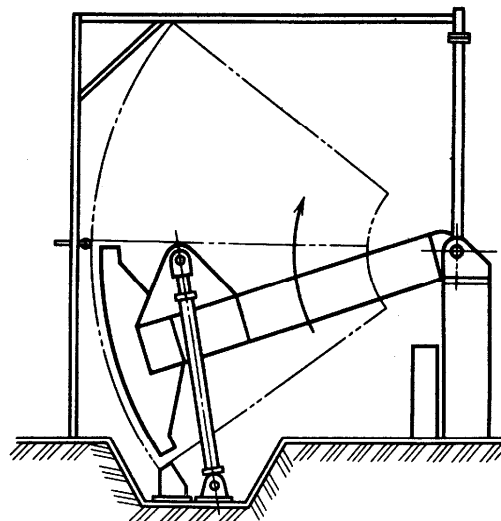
Стенд для электрошлаковой сварки или дуговой сварки с принудительным формированием шва
